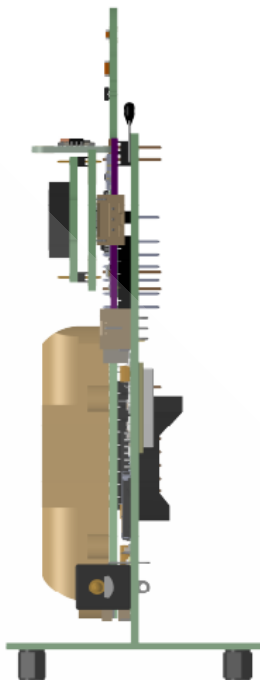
แสดง Dimension PCBA ของ IEQ sensor
